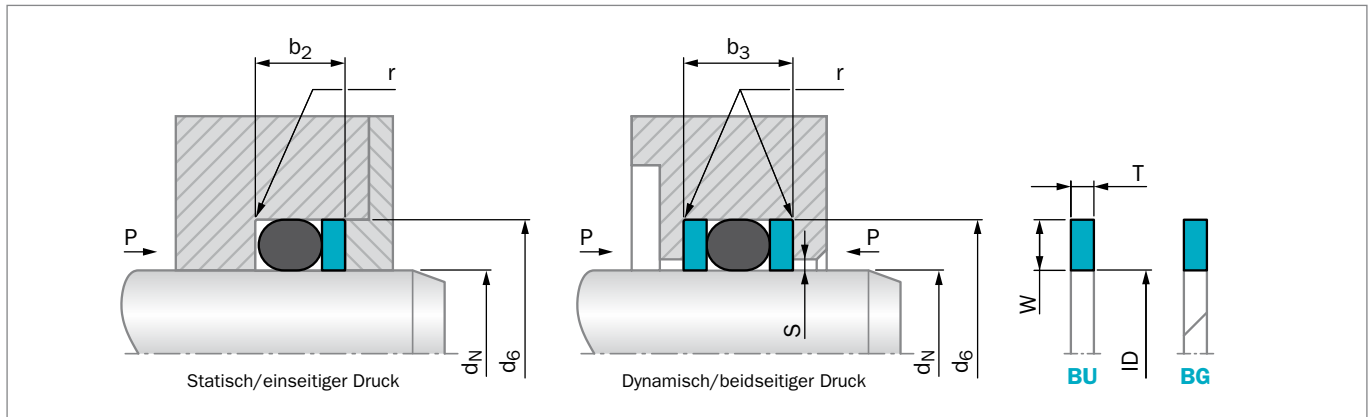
Einbauzeichnung innendichtend, rechteckige Stützring-Typen
